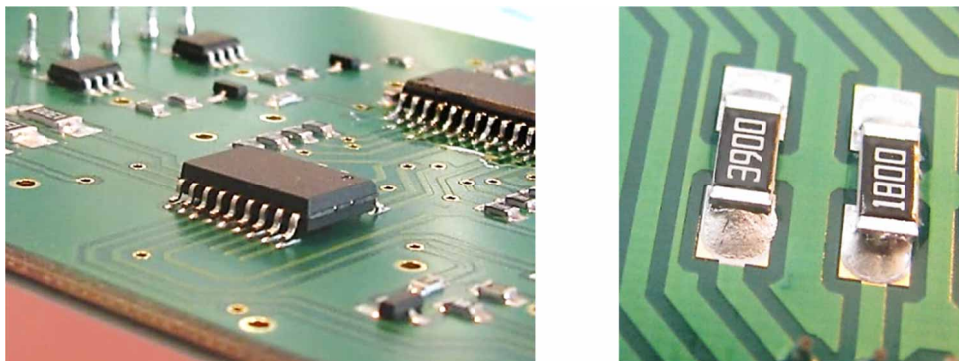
Osazená rozšiřující deska a odstranění chyby
